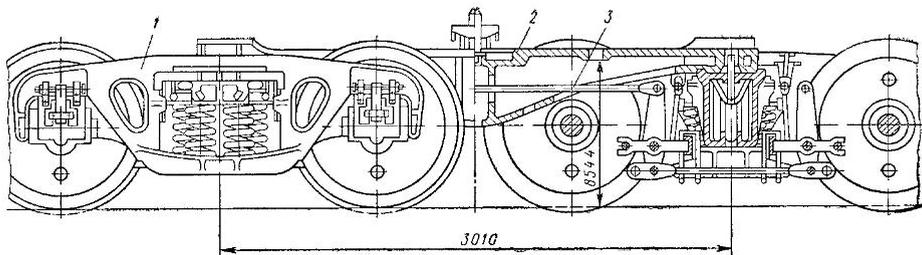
Четырехосная тележка со штампосварной соединительной балкой и буксами на подшипниках качения.
